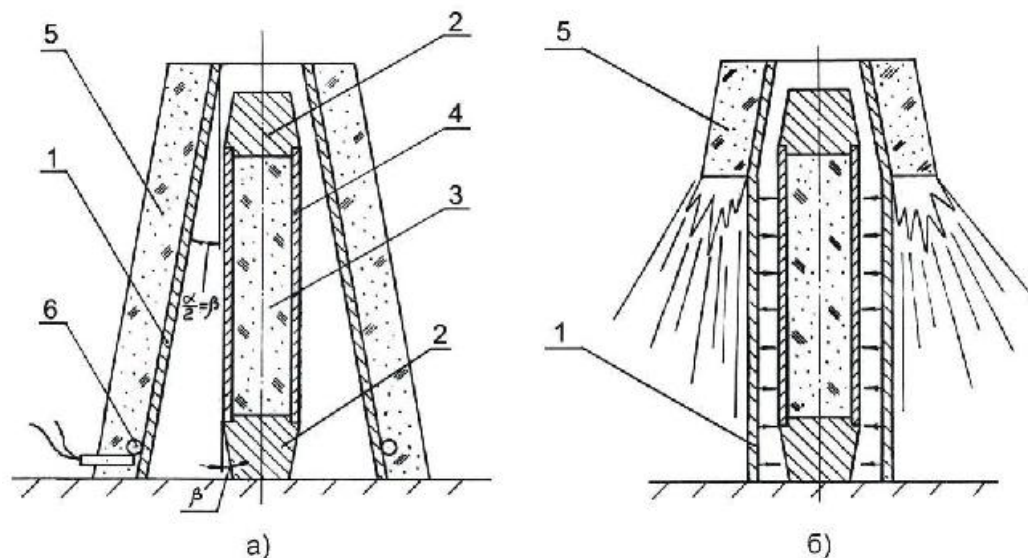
Схема прессования трубчатых заготовок наружными зарядами до нагружения (а), в процессе нагружения (б)
